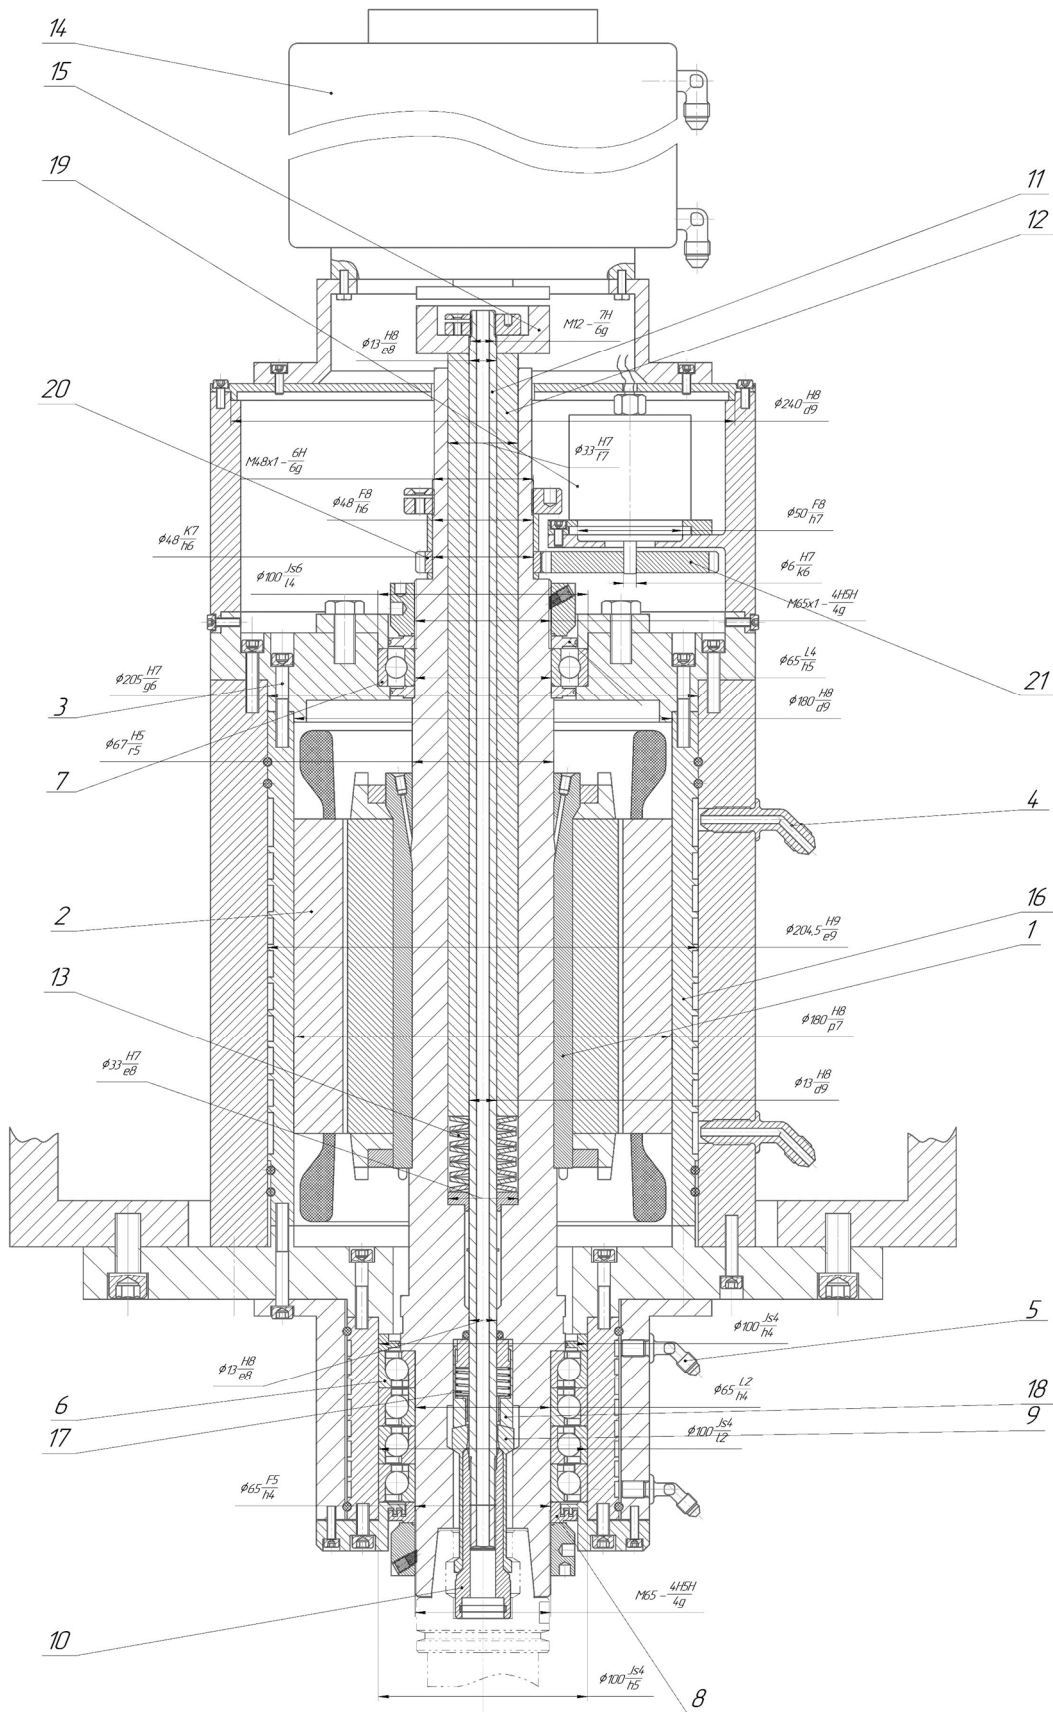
Шпиндельний вузол багатощільового верстата
